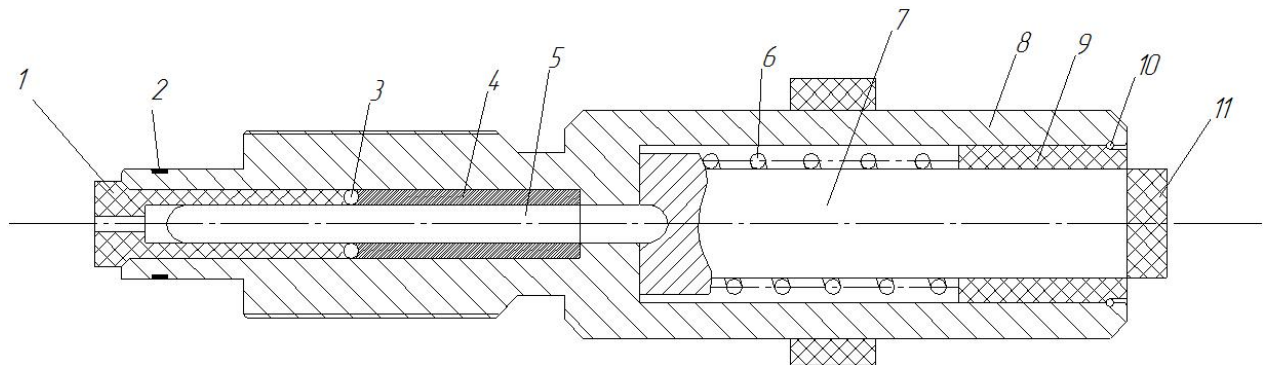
Індикатор тиску типу ІДЗ : 1 - пробка; 2, 3, 10 - кільця; 4 - вальниця; 5 - ролик; 6 - пружина; 7,11 - вказівники тиску поточного та найбільшого; 8 – корпус; 9 - заглушка.
